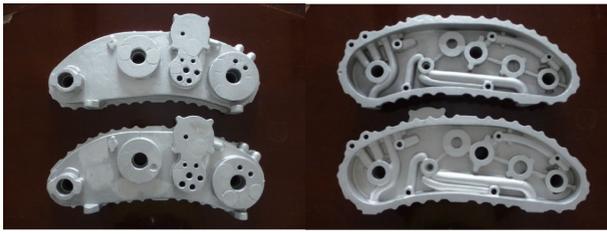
某新型发动机机匣盖(尺寸为 500 mm×220 mm×50 mm)
